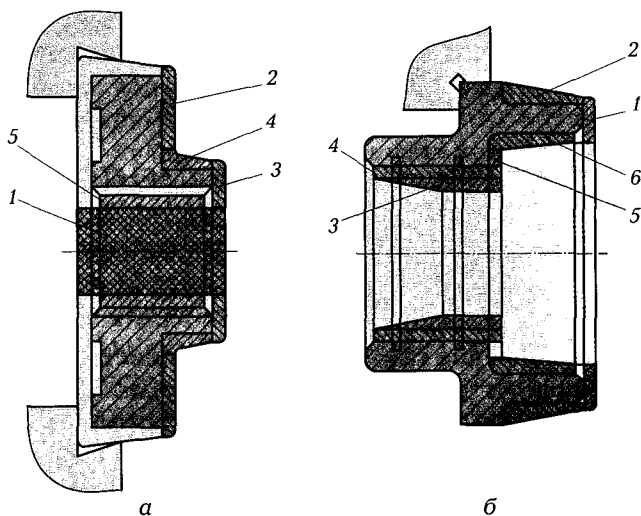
Последовательность обработки заготовки в трехкулачковом патроне:
